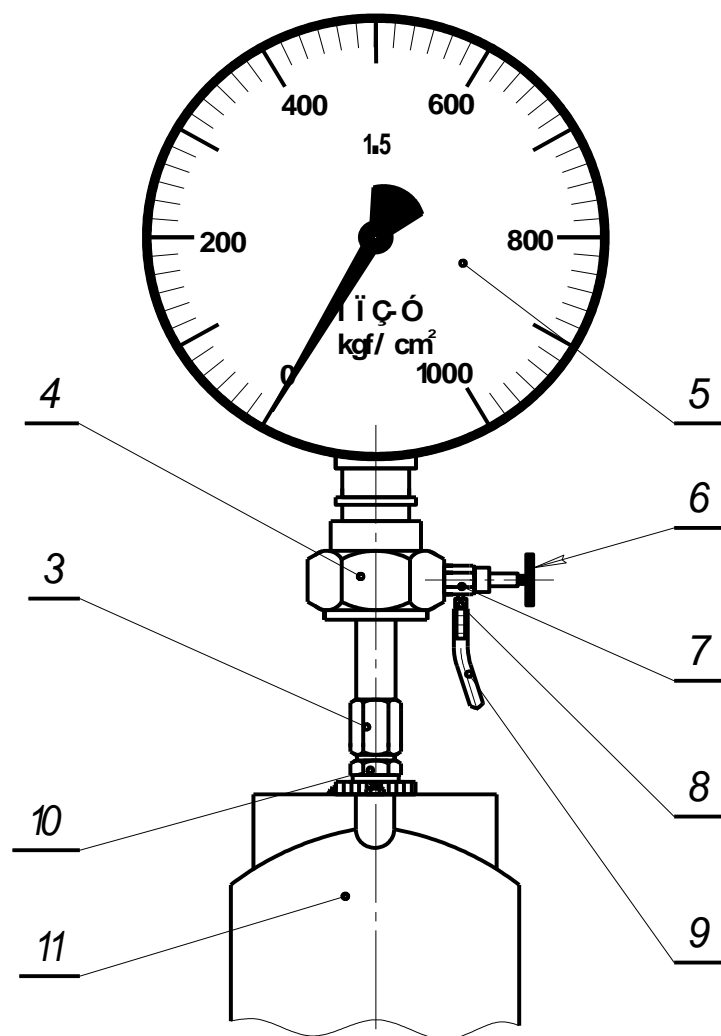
Установка дизельтестера ТАД-01А на ТНВД «напрямую» – при помощи накидной гайки: 1 – рукав высокого давления; 2 – штуцер проходной; 3 – гайка накидная; 4 – корпус; 5 - манометр; 6 – винт вентиля; 7 – гайка вентиля; 8 – ниппель; 9 – рукав сливной; 10 – штуцер нажимной ТНВД; 11 - ТНВД
